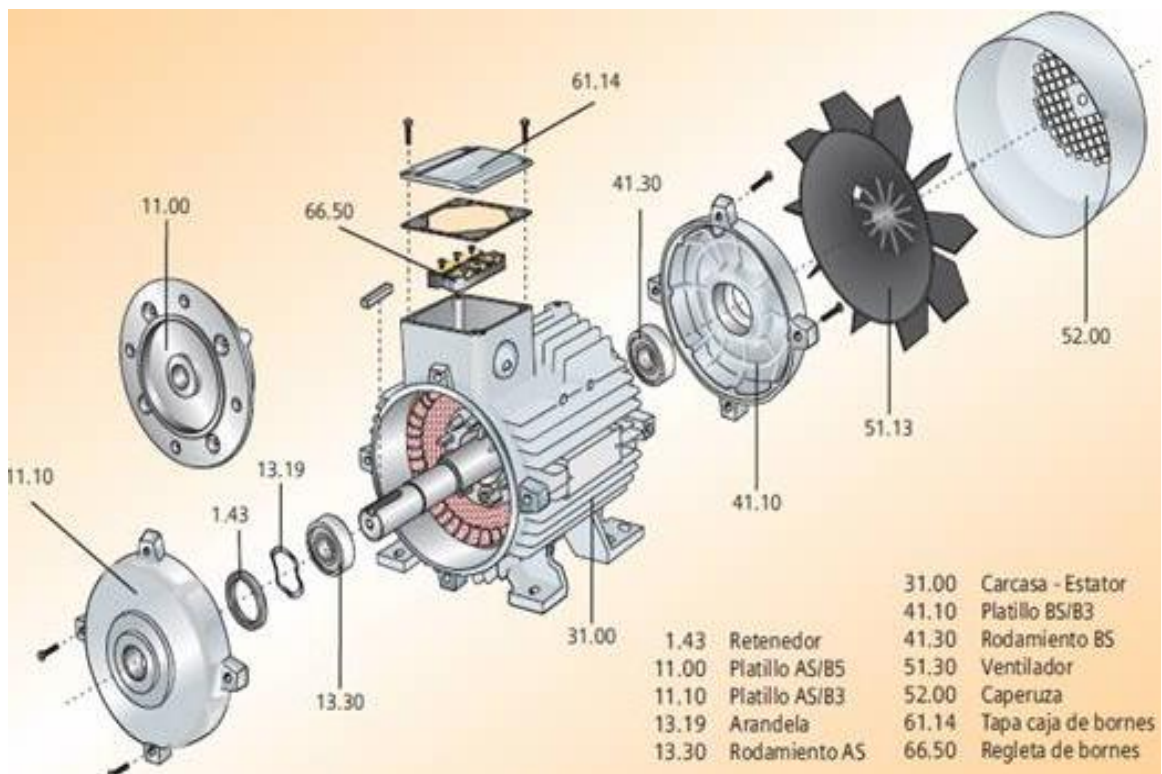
Motor Trifásico 1LA7 080-4YA60 y sus Partes
